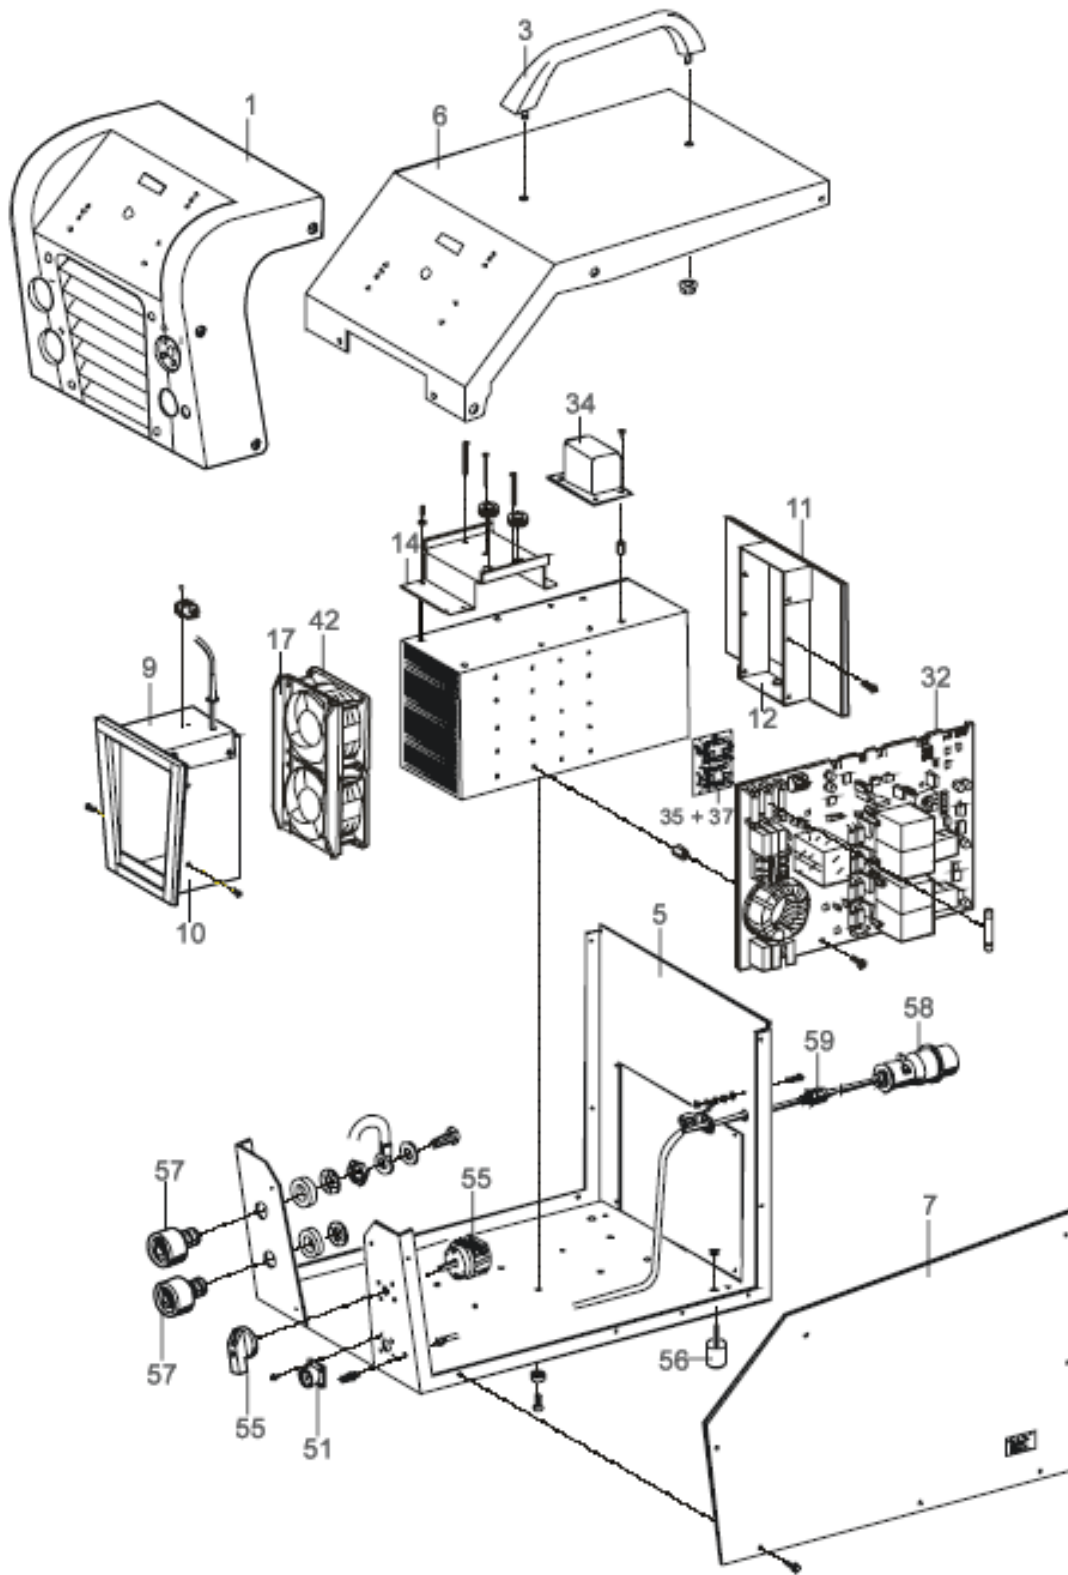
Explosietekening RODIE 250 - 320 (rechts)
